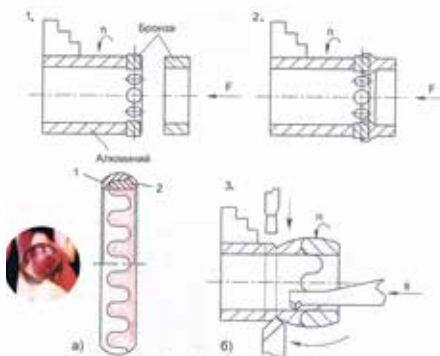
Биметаллическое кольцо – а) и способ его изготовления; – б). 1, 2 и 3 – позиции обработки; п – вращение заготовки, F – сила поджима кольца, s – подача расточного резца
